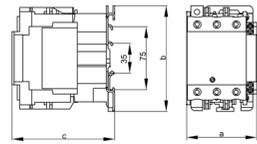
Габаритные размеры контакторов ПК-465XX — ПК-495XX
